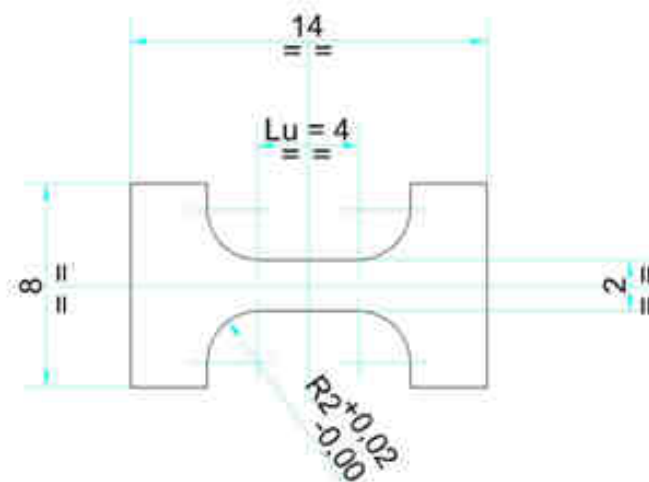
Dimension des éprouvettes pour la machine de traction de 10 tonnes.
